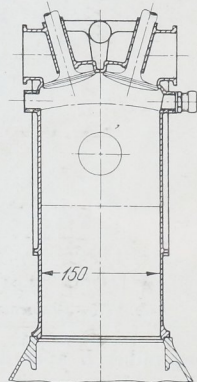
Leichtmotorzylinder mit schräg angeordneten Ventilen im Kopf.
